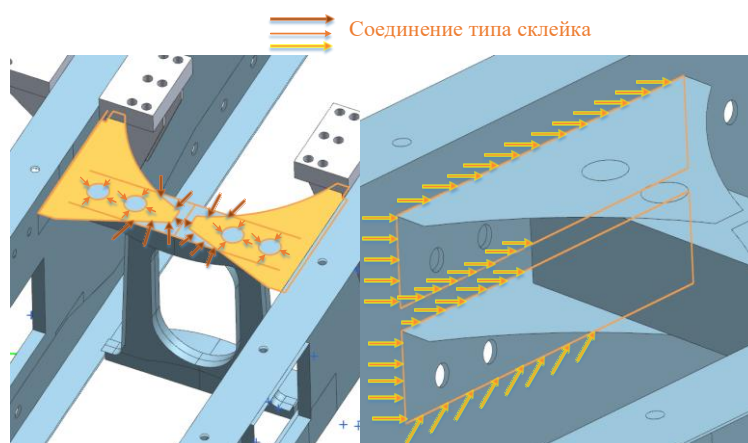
Моделирование сварных швов в конструкции лонжеронов
